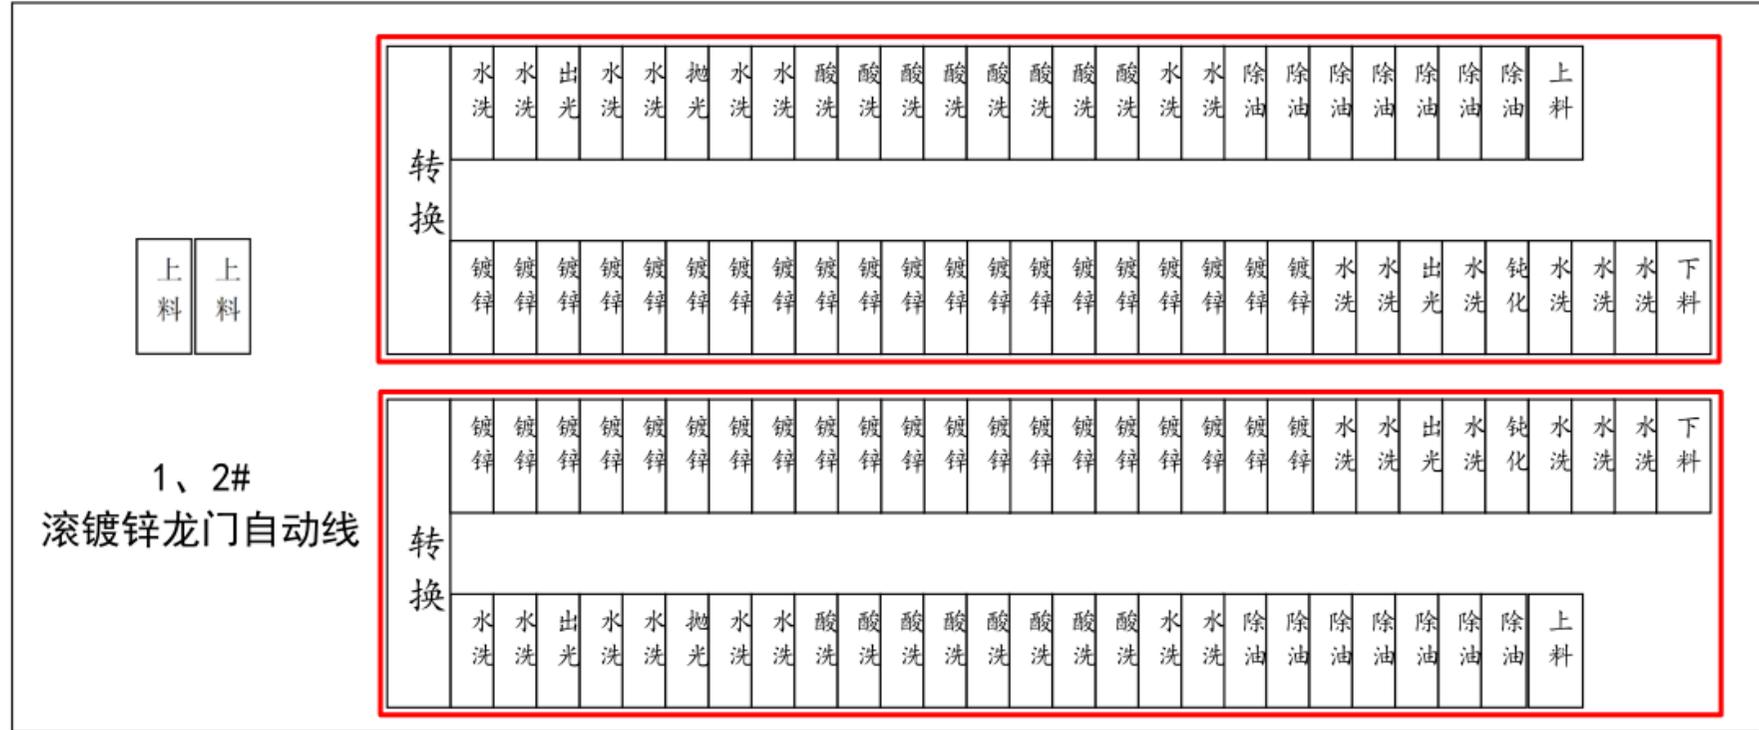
A 栋生产厂房 1 楼 2 车间平面布置图
